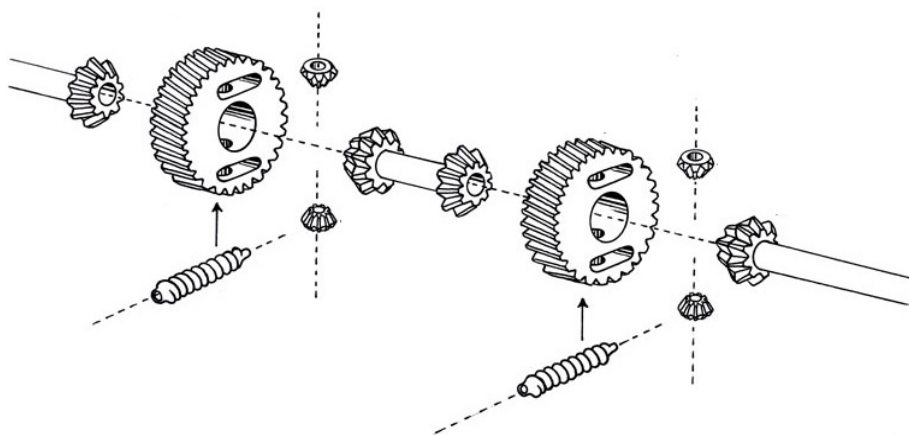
Vista explodida do trem de engrenagens [Ballester, 2008].
